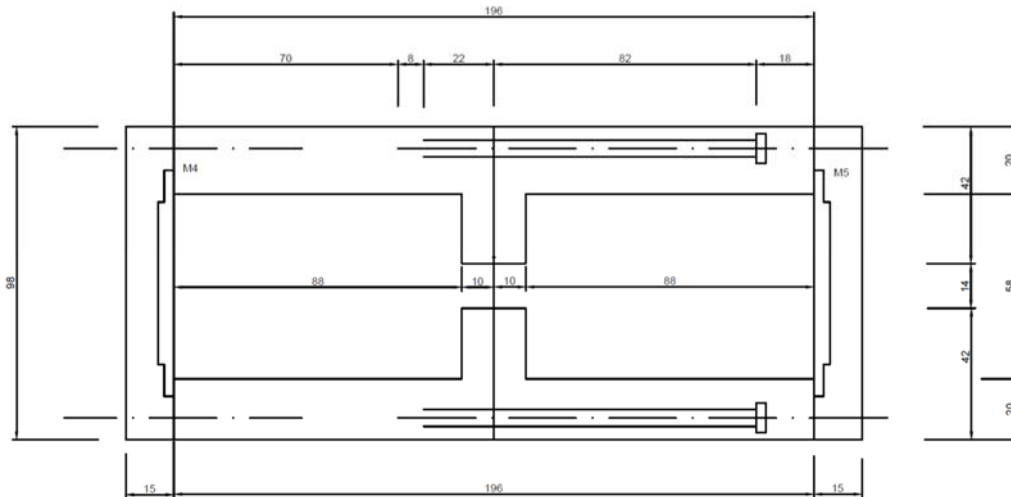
Grundriss der Konstruierten Zelle, erstellt mit AutoCAD.
